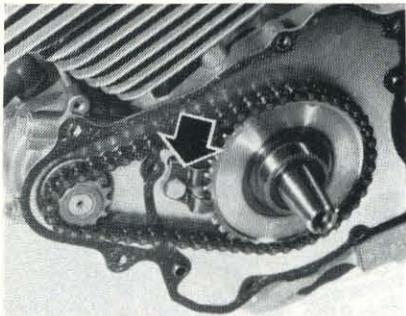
Patte de calage latéral du pignon de démarrage (Photo RMT)
